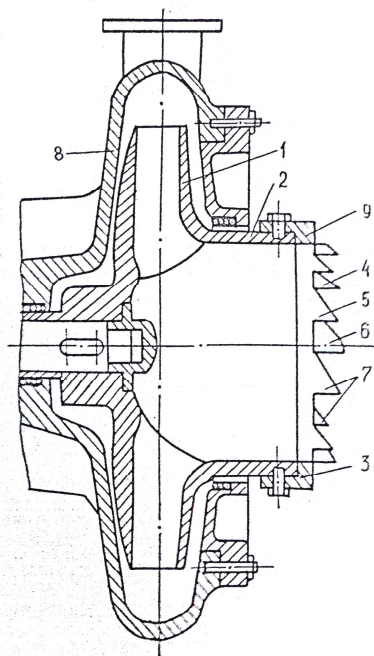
Схема насоса с режущим устройством в виде зубьев (1 – рабочее колесо; 2 – всасывающая горловина; 3 – торец; 4-6 – зубья; 7 - режущие кромки; 8 – корпус; 9 - кожух).
